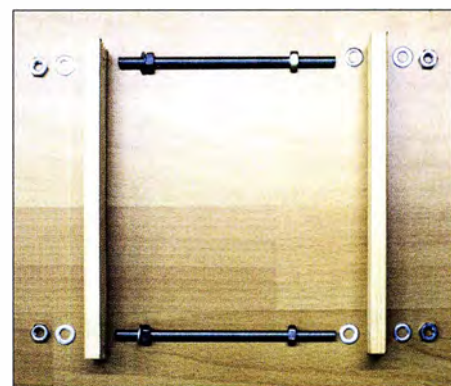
Für den Platinenhalter sind nur diese wenigen Teile nötig.
